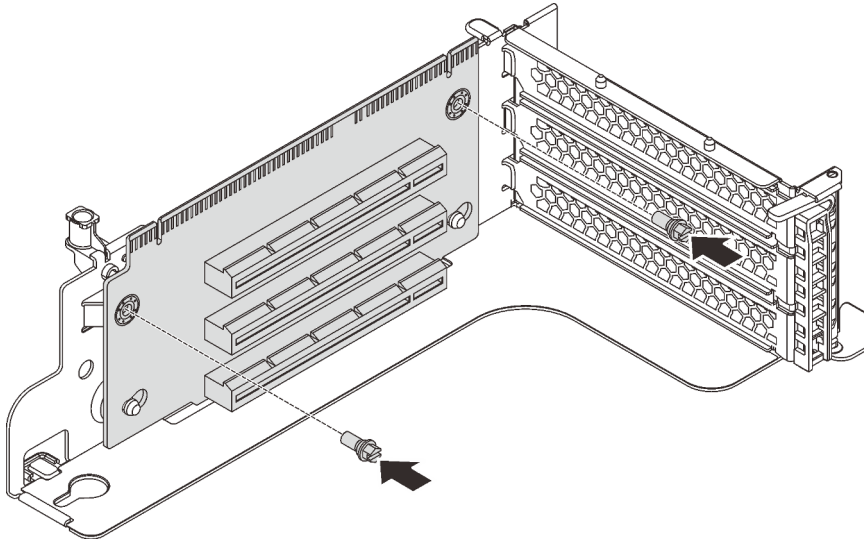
Schrauben zum Befestigen der Adapterkarte anbringen
